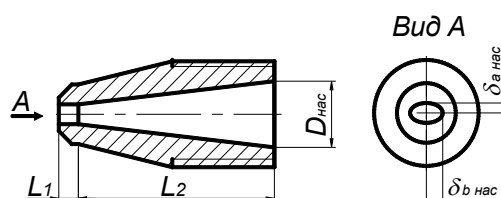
Схема конідального насадка з еліптичним вихідним отвором:
